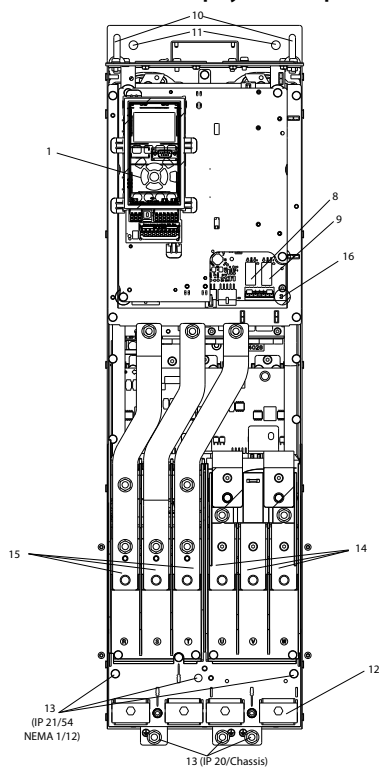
Внутренние компоненты корпуса типоразмера D
